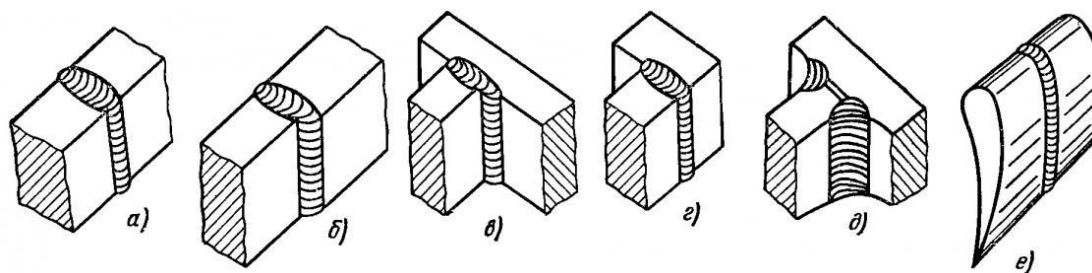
Основные типы сварных соединений, выполняемых электрошлаковой сваркой:
